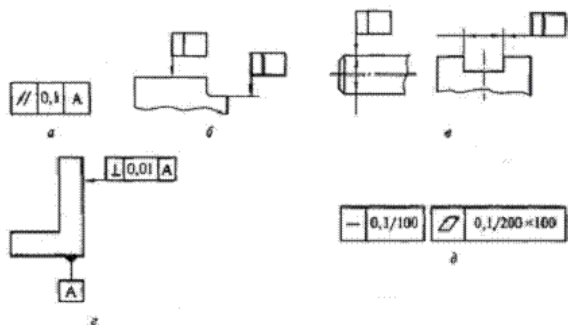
Условные обозначения допусков расположения и формы на чертежах
